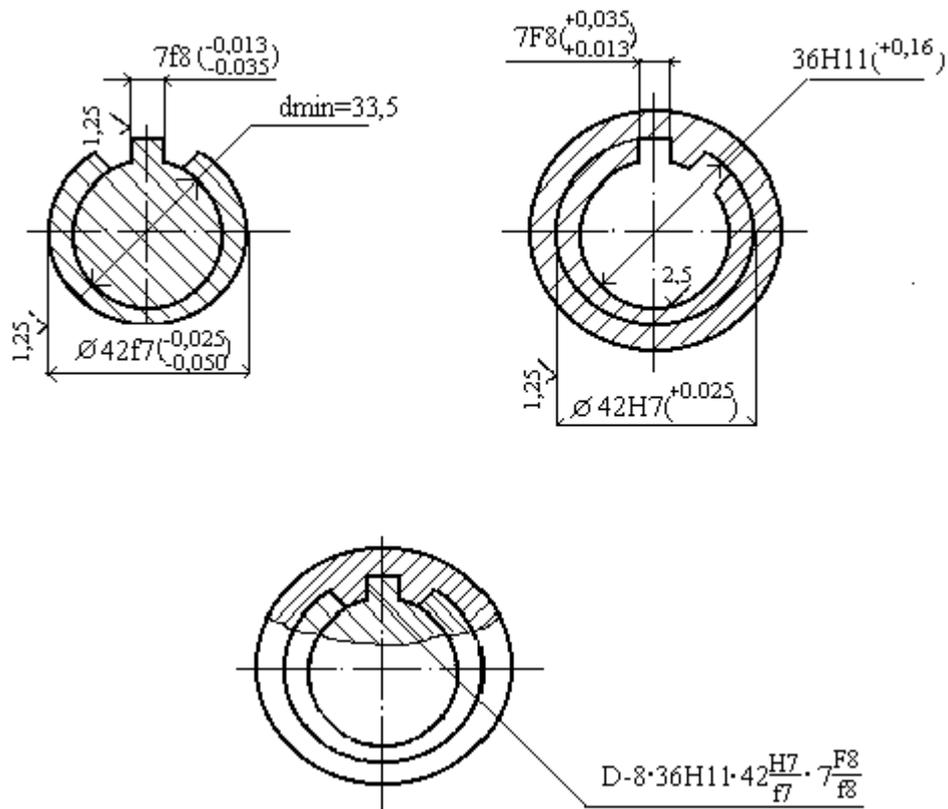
Обозначение допусков и посадок шлицевого соединения на рабочих и сборочных чертежах
